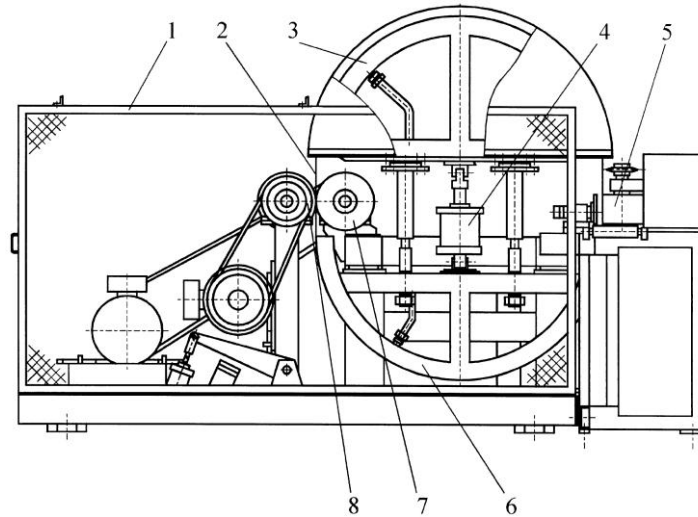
Ленточнопильный станок с пилой, движущейся по криволинейным аэростатическим направляющим: 1 – ограждение; 2 – пила; 3, 6 – верхняя и нижняя криволинейные аэростатические направляющие; 4 – механизм натяжения пилы; 5 – механизм подачи; 7, 8 – приводные фрикционные колеса
